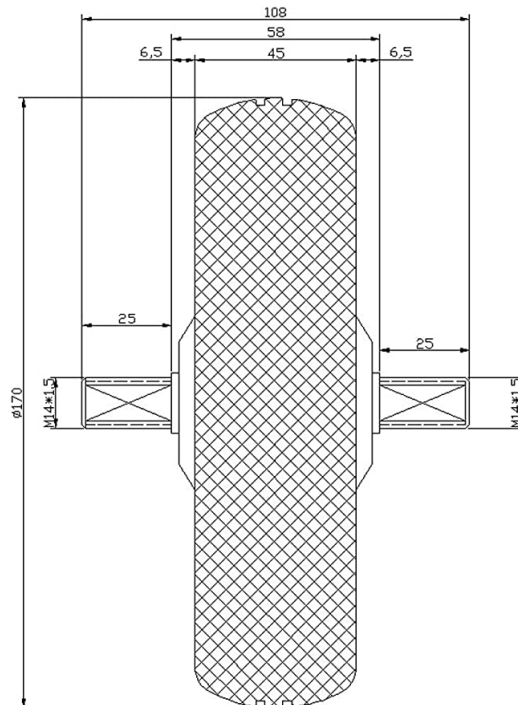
Les dimensions de de BLDC Hub motor
